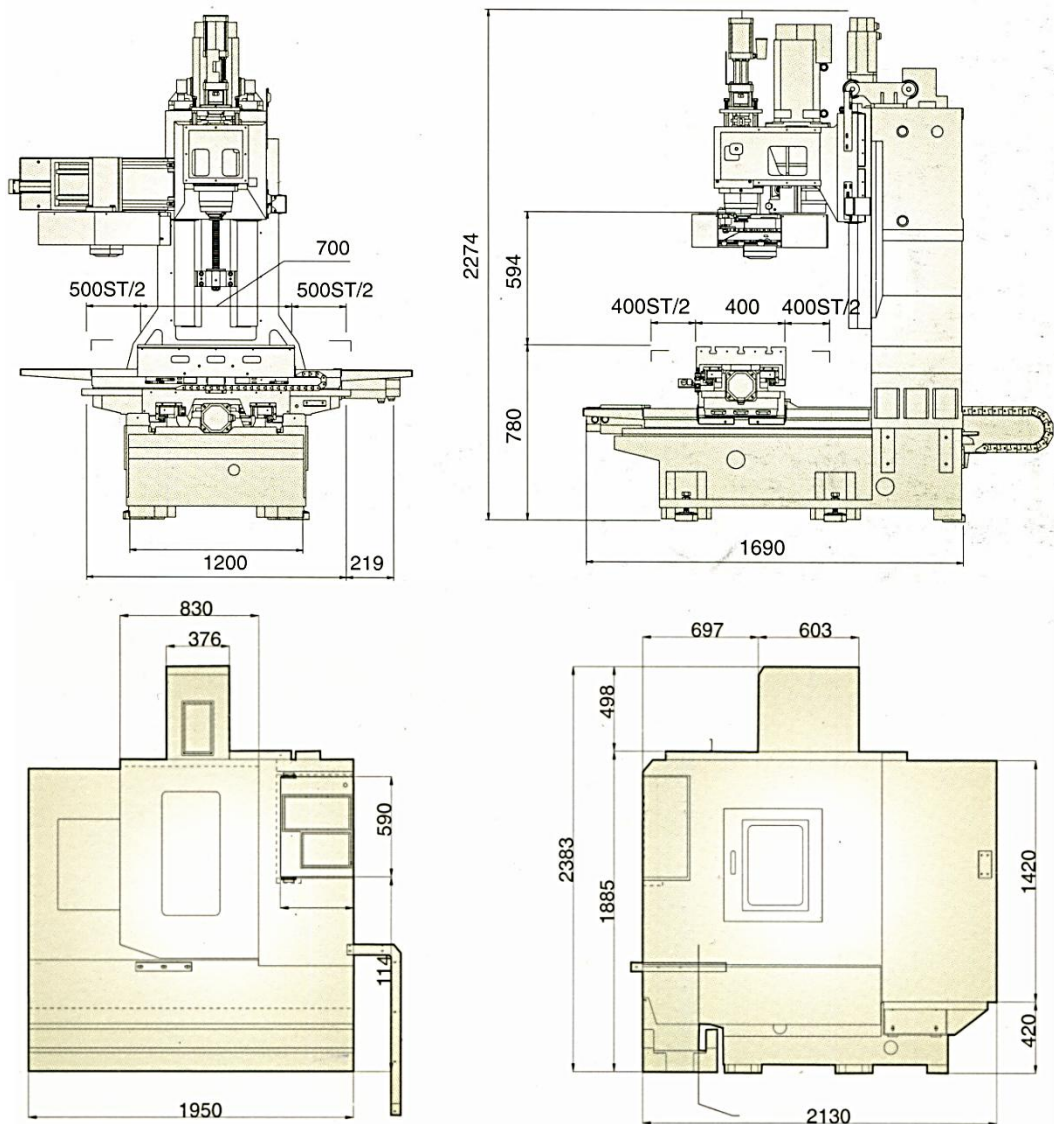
Зовнішній вигляд вертикального оброблювального центра VA 500 з габаритними розмірами.
